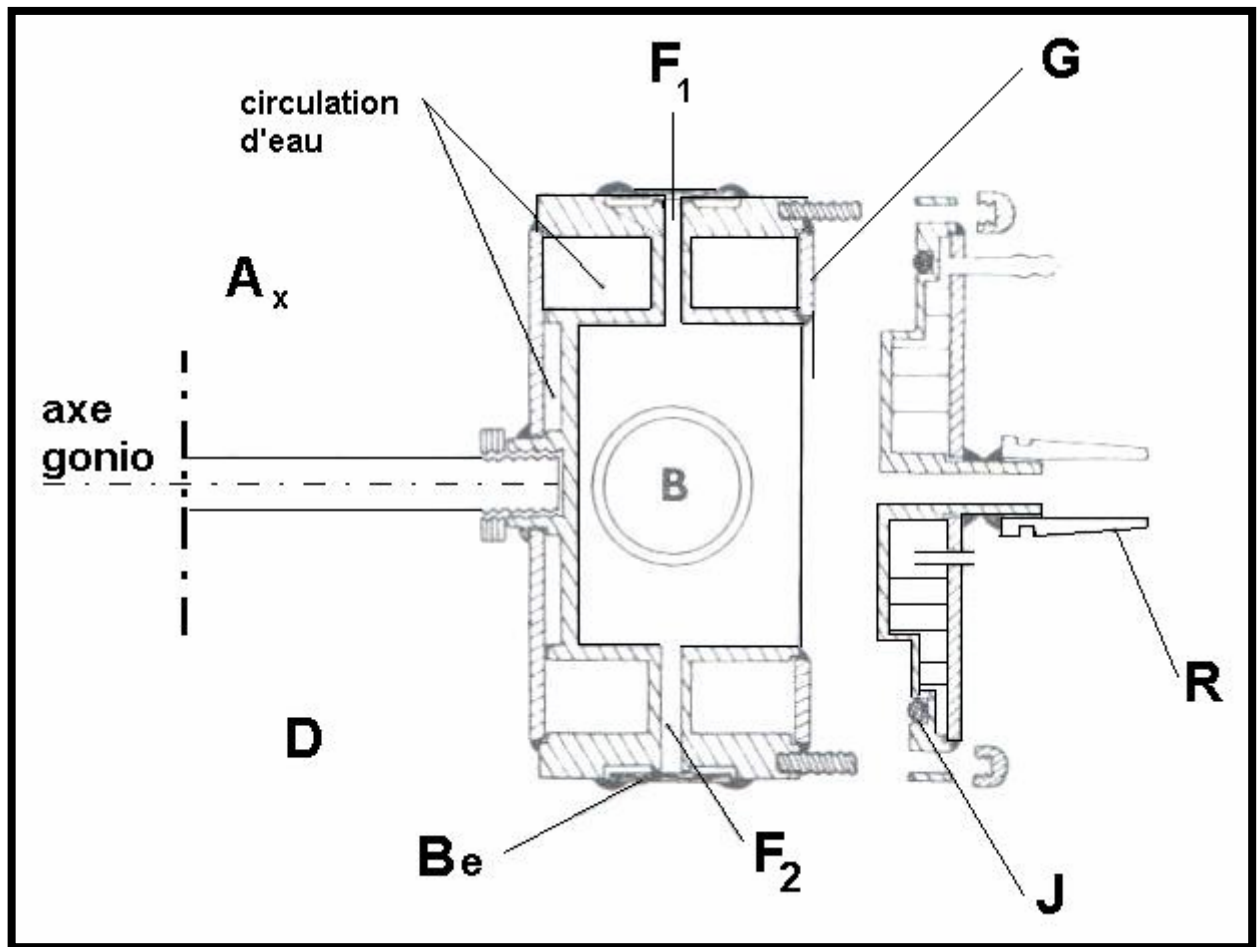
Coupe transversale de la chambre et du couvercle. Vue de dessus.
